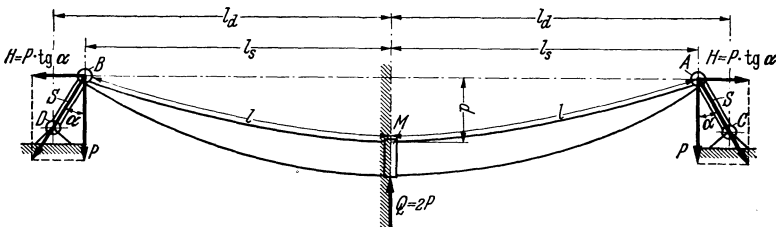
Geschichtete Blattfeder mit schrägem Lastangriff.
